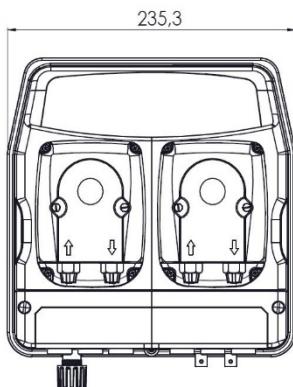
Ansichten und Abmessungen - Schlauchpumpe
